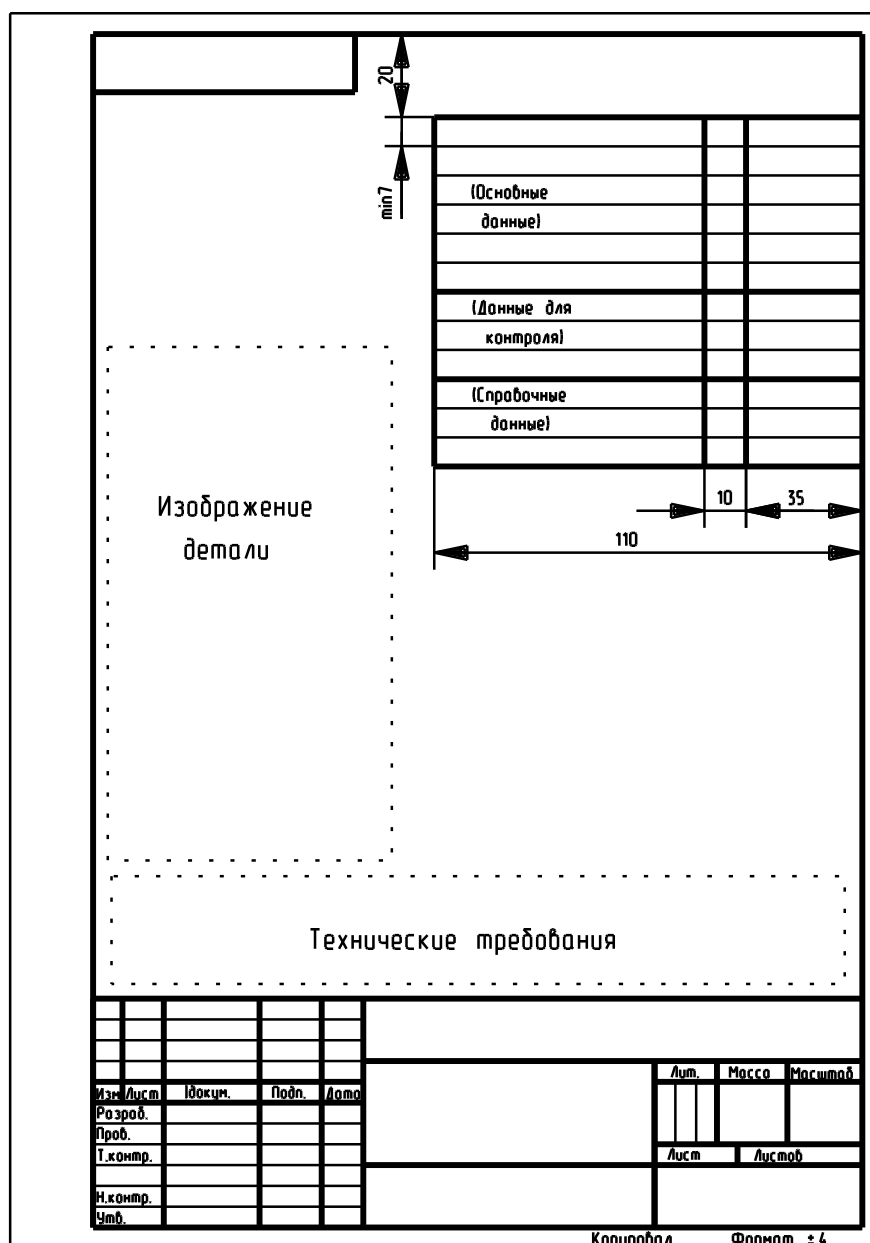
Компонировка чертежа зубчатого колеса
